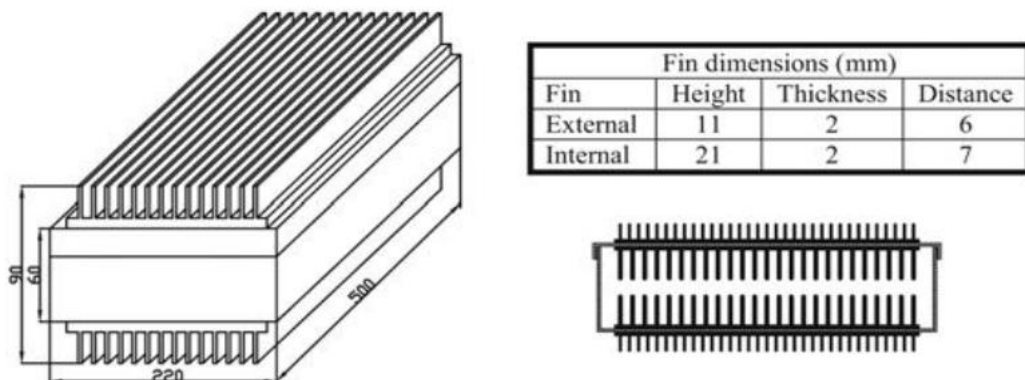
Forme et section transversale de la chambre froide avec dimensions des ailettes [17]
